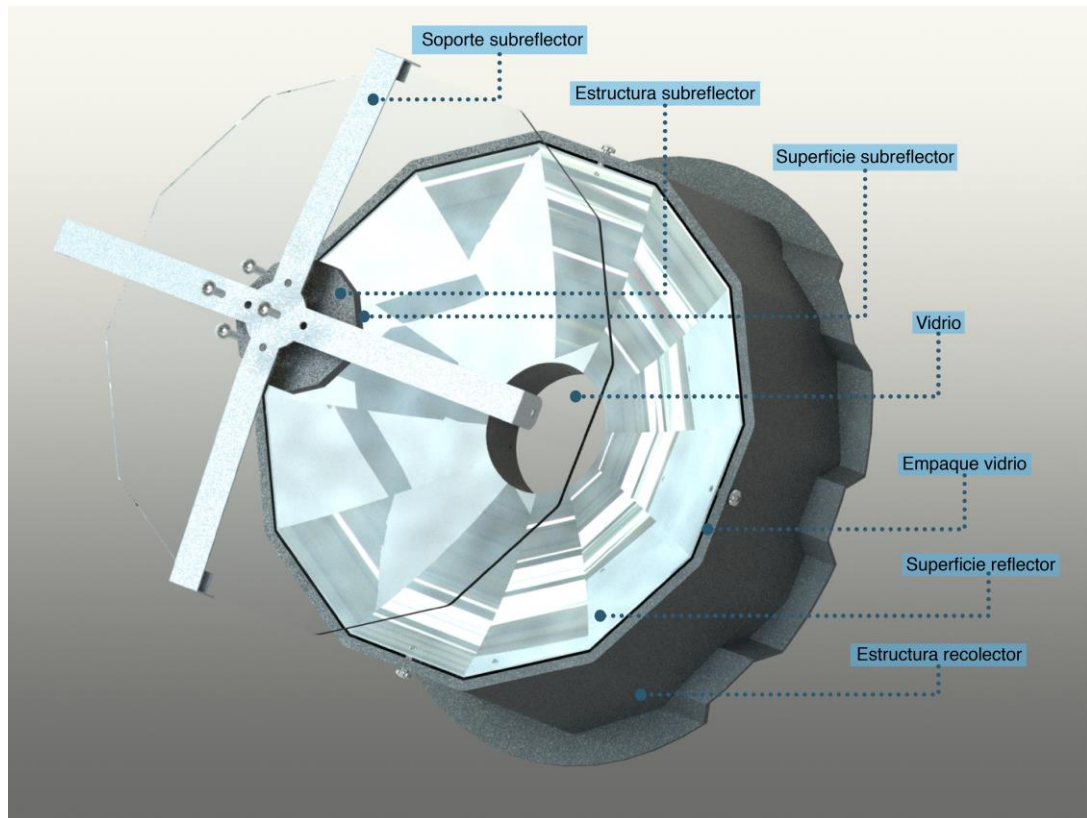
Vista explosionada recolector. Fuente: Autora.
